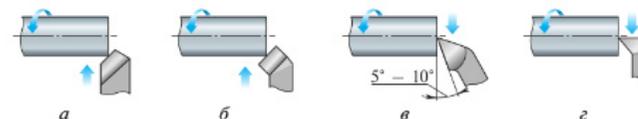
Подрезание торца: *a* — проходным прямым резцом; *б* — проходным отогнутым резцом; *в* — проходным упорным резцом; *г* — подрезным резцом
